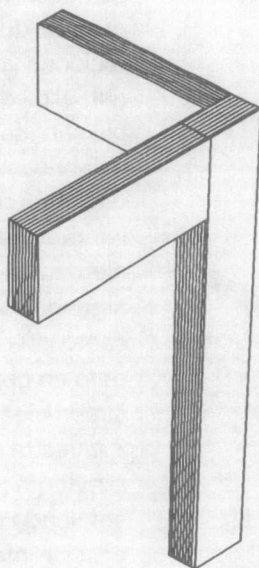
Posible aplicación de LVL en la construcción de partes para sillas de madera.
